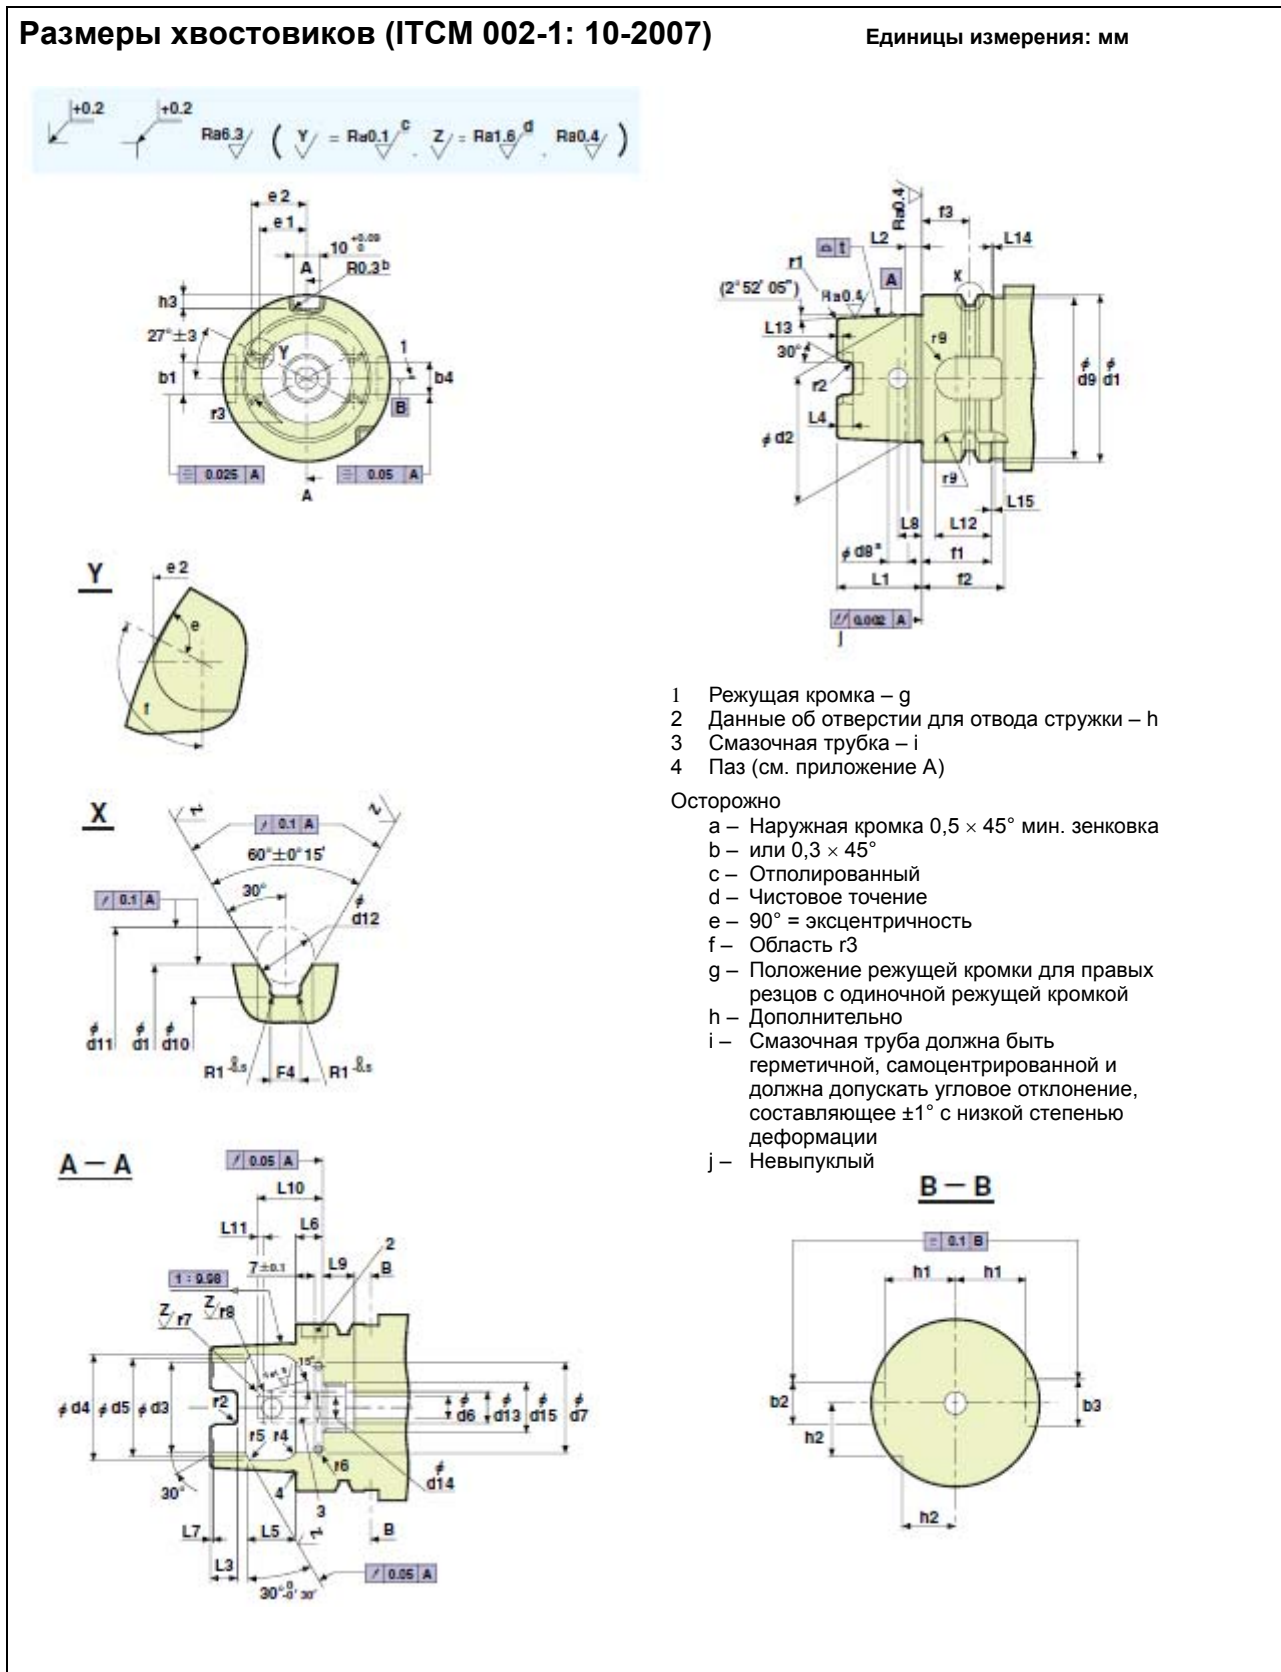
Номинальные размеры базовых оправок HSK-A63 (ICTM)
